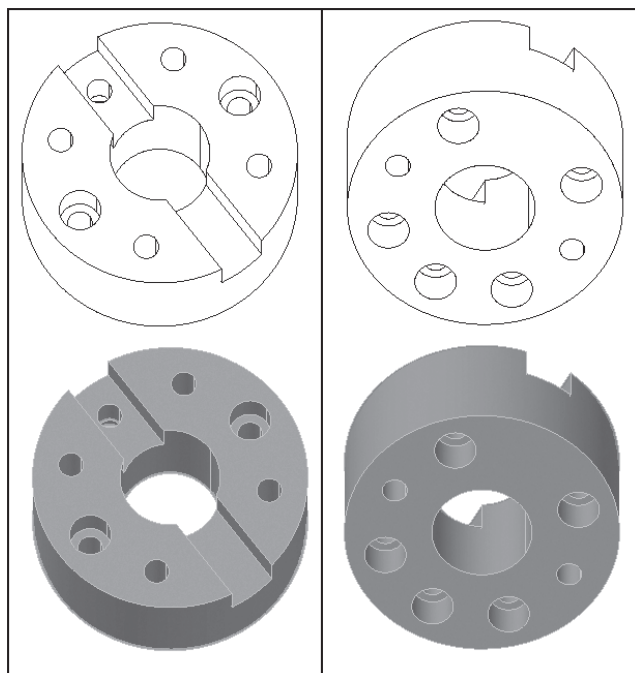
Примеры изображения 3D-модели детали «Корпус» в двух ракурсах и двух разных визуальных стилях Скрытый и Тонированный
